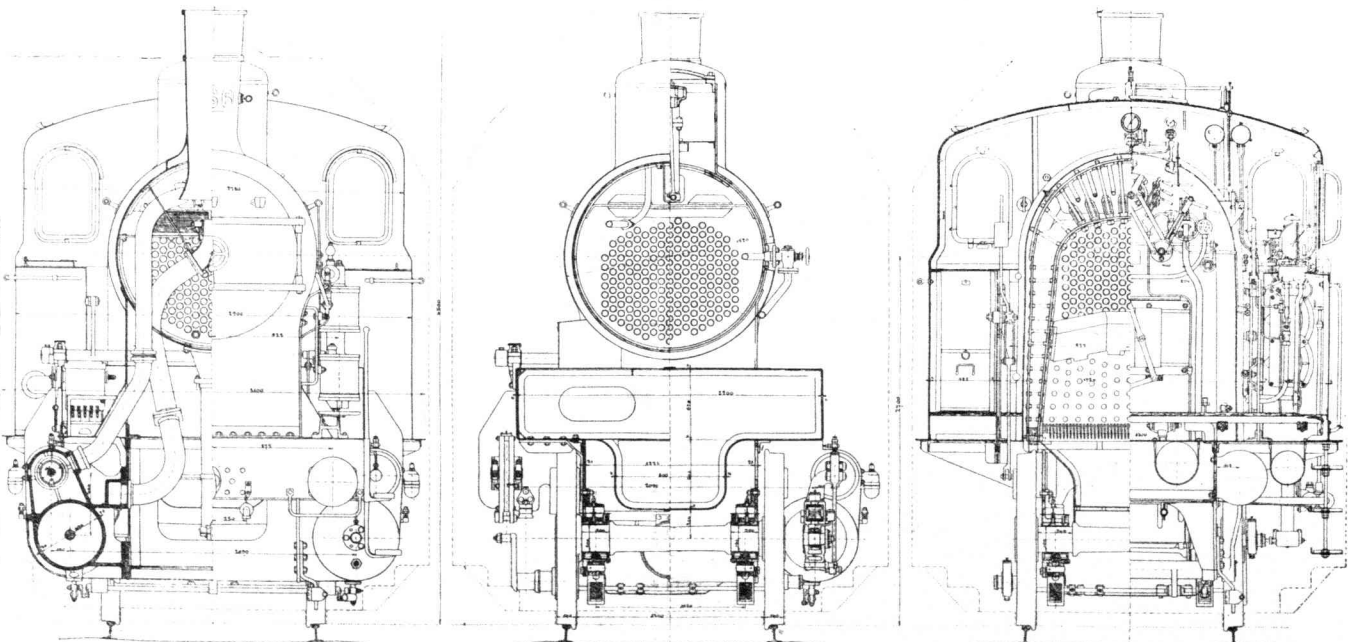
Querschnitte und Stirnansichten zu Abb. 2.
